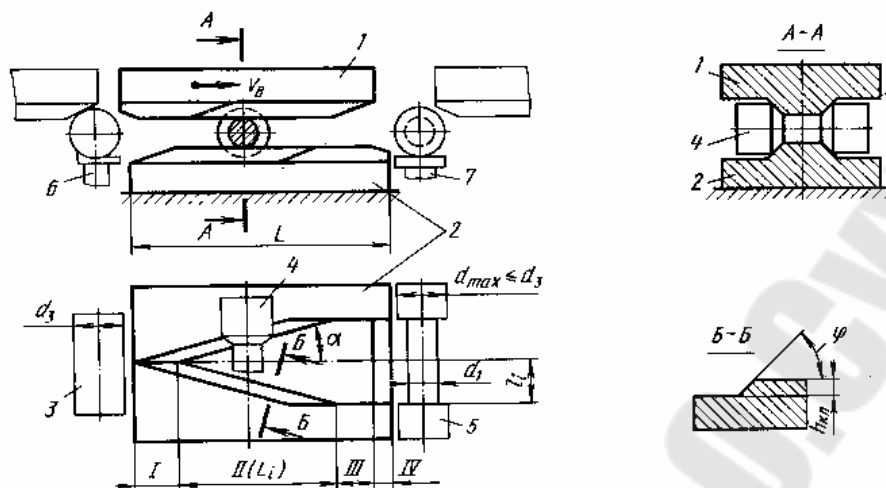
Схема поперечной клиновой прокатки с подвижной и неподвижной частями инструмента:
